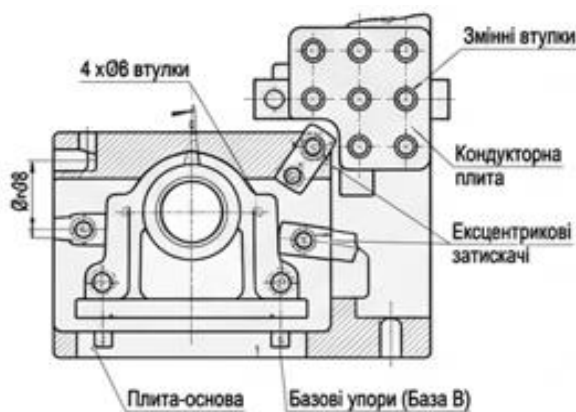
Кондуктор для фрезерування та свердління
